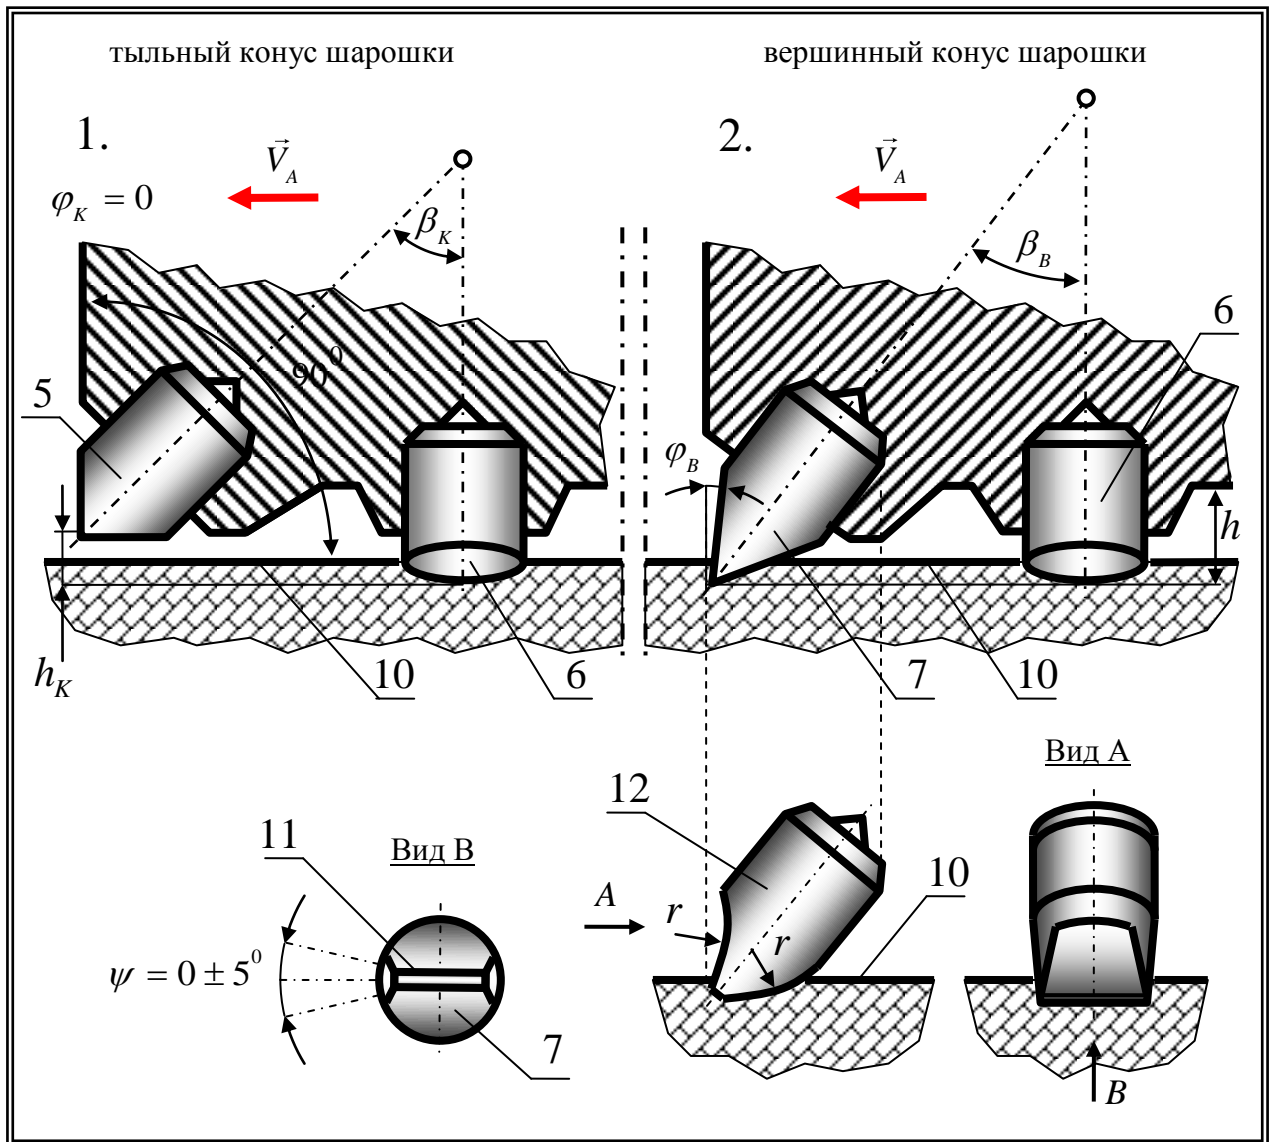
Схема расположения твердосплавных зубков на калибрующем (тыльном) и вершинном конусах шарошек
